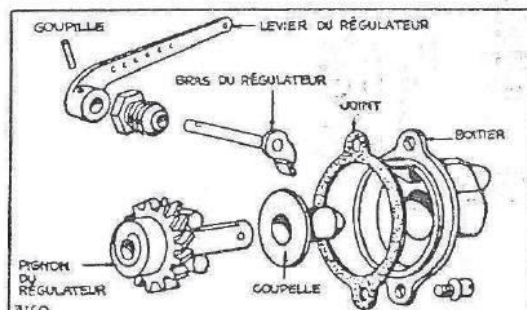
Boîtier du régulateur et assemblage du pignon
